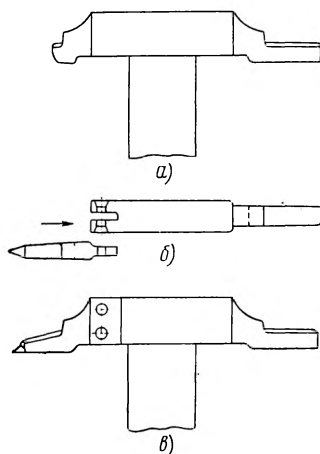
Схема ремонта губки штанги точного штангенциркуля
